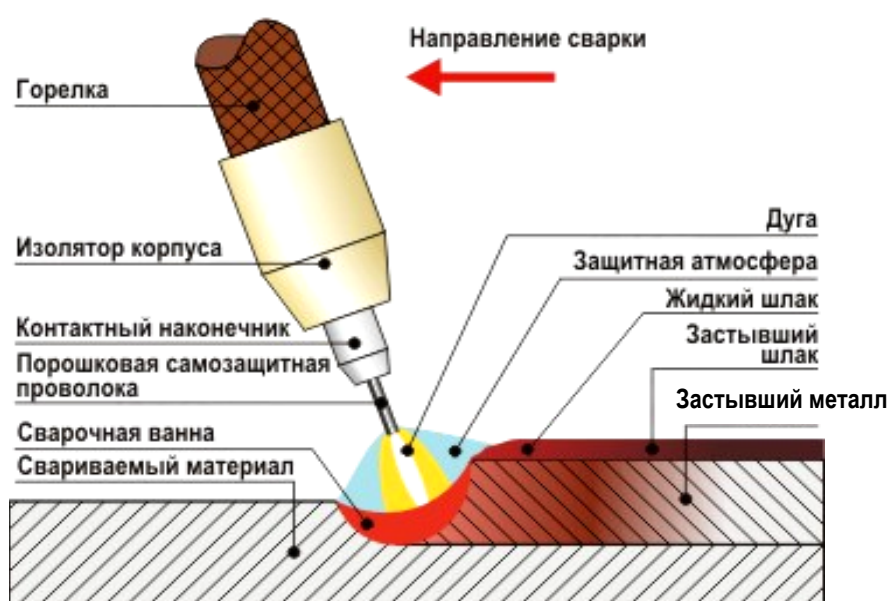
Схема сварки самозащитной порошковой проволокой
